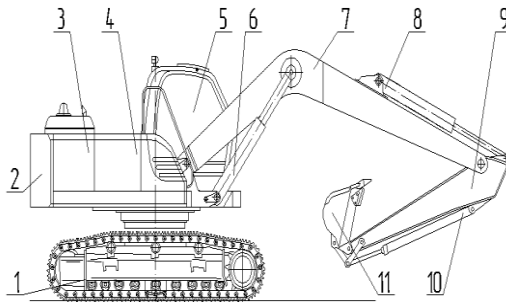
Устройство экскаватора с рабочим оборудованием обратная лопата:
